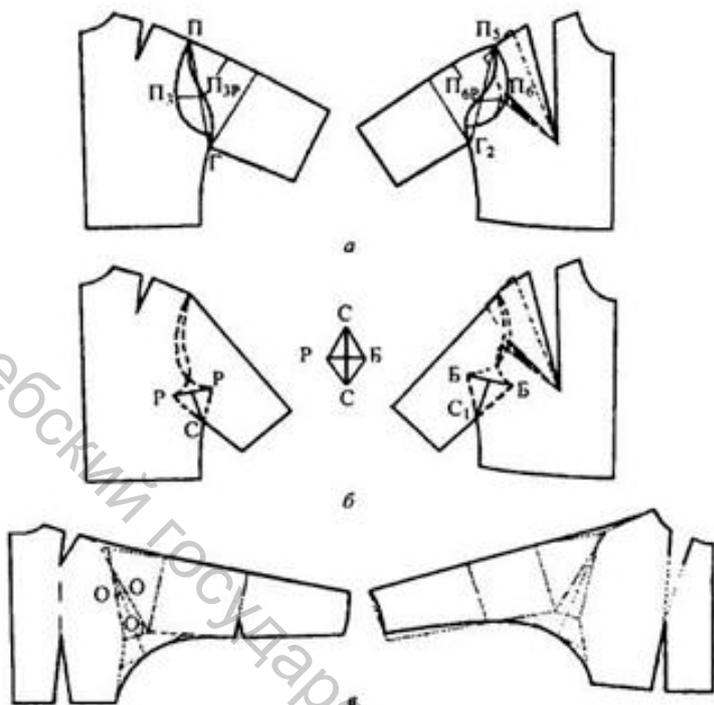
Схемы чертежей деталей с цельнокроеными рукавами:
